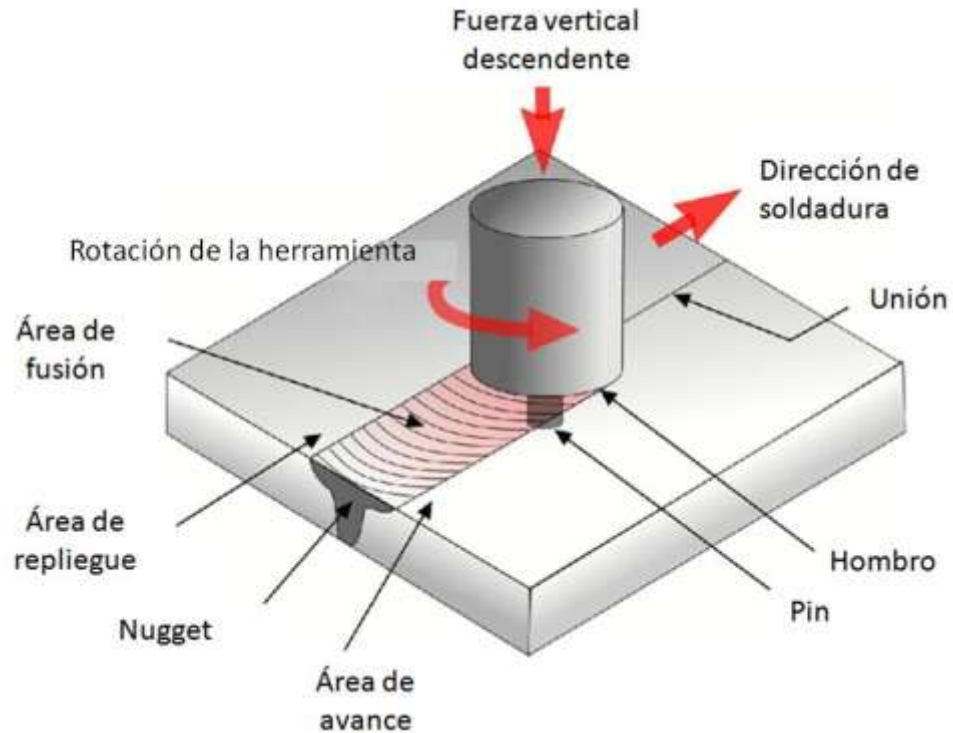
Esquema del proceso de soldadura por fricción ⁽⁵⁾
